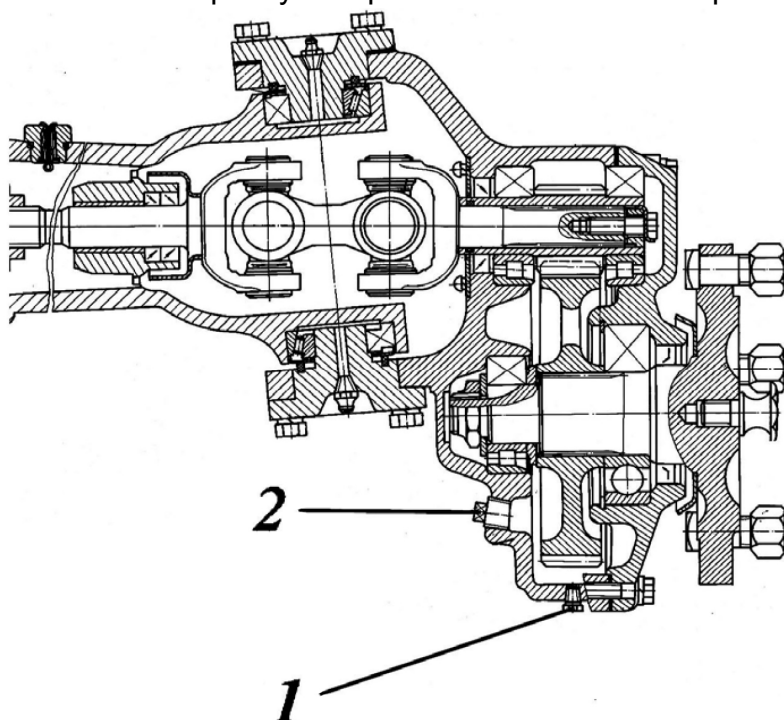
(#) – Проверка уровня масла в корпусе главной передачи ПВМ.
